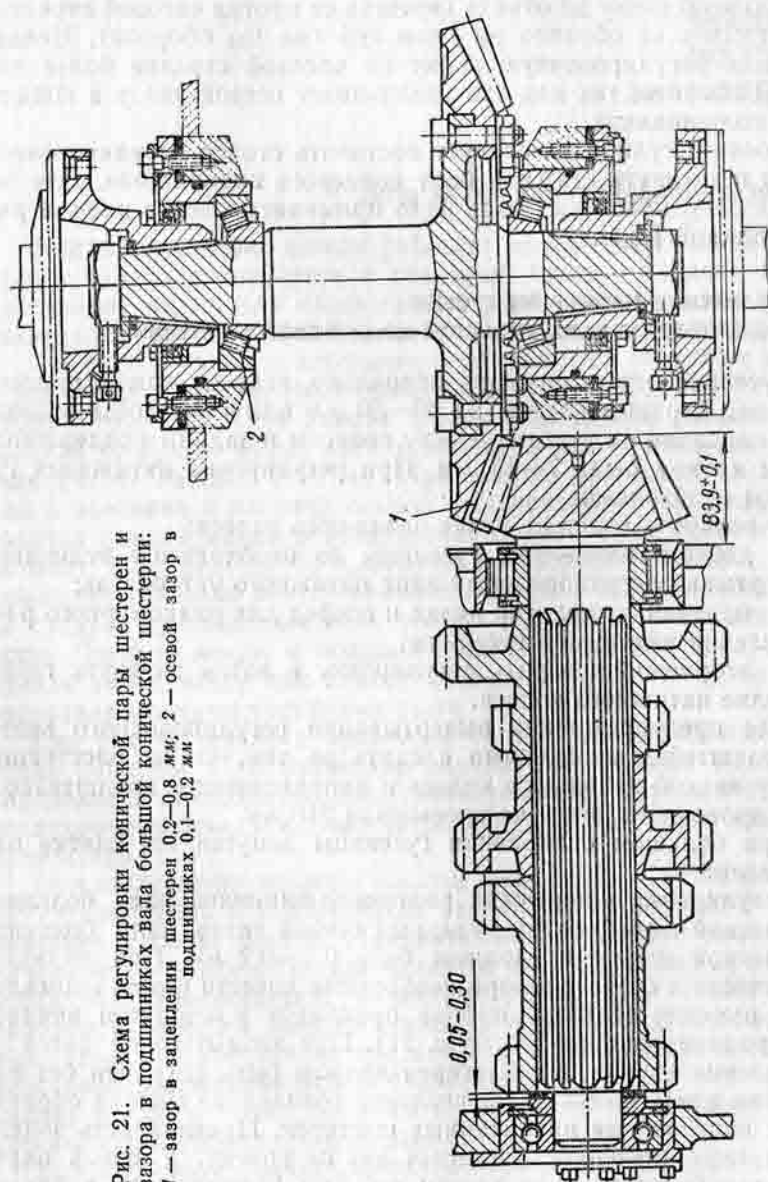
Схема регулировки конической пары шестерен и зазора в подшипниках вала большой конической шестерни: 1 — зазор в зацеплении шестерен 0,2—0,8 мм; 2 — осевой зазор в подшипниках 0,1—0,2 мм
